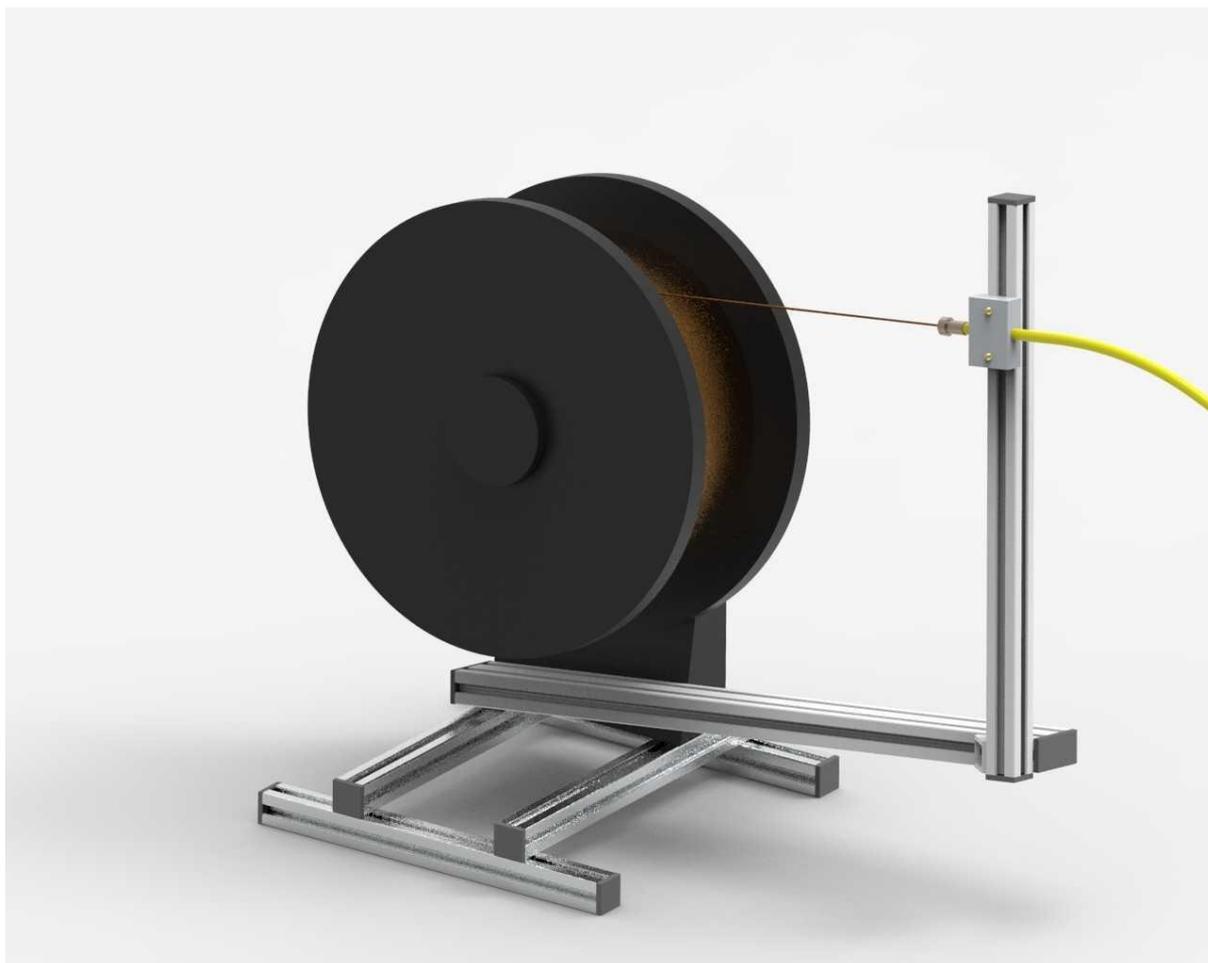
Внешний вид держателя катушки присадочной проволоки
